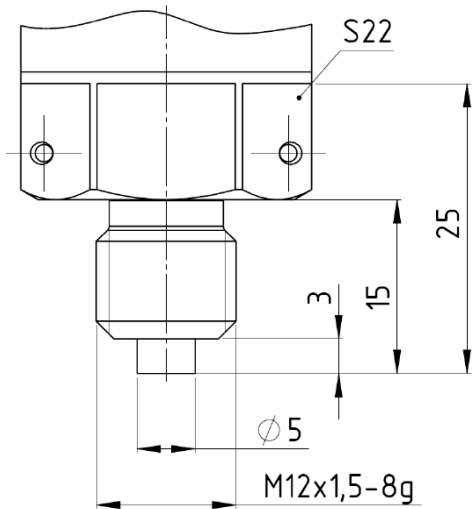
Присоединительный штуцер тип 1 по ГОСТ 2405-88, черт. 20
